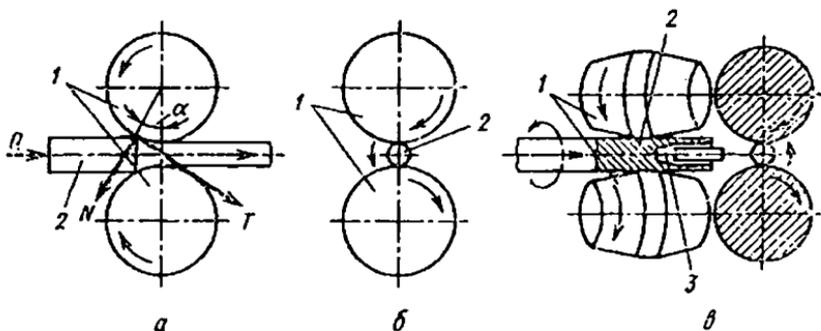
Основные виды прокатки: а — продольная; б — поперечная; в — поперечно-винтовая: 1 — валки; 2 — заготовка; 3 — прошивень на неподвижной оправке
